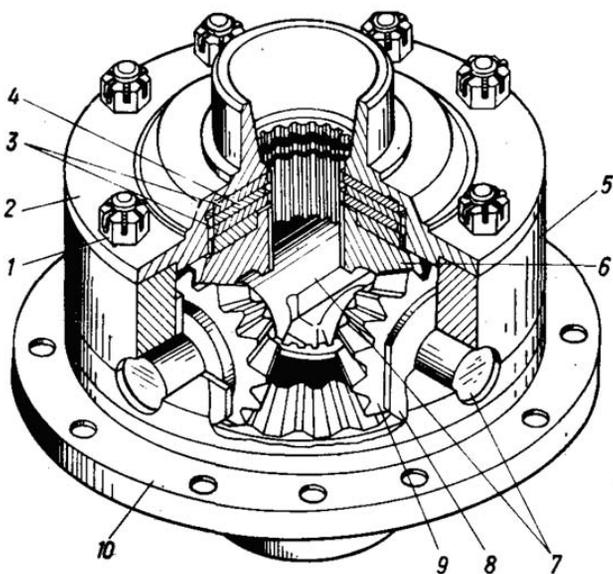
Снятие ведомого зубчатого колеса: 1 — гайка; 2 — фланец; 3 — диск ведущий; 4 — диск ведомый; 5, 10 — корпус; 6 — колесо зубчатое; 7 — ось; 8 — шайба; 9 — сателлит
